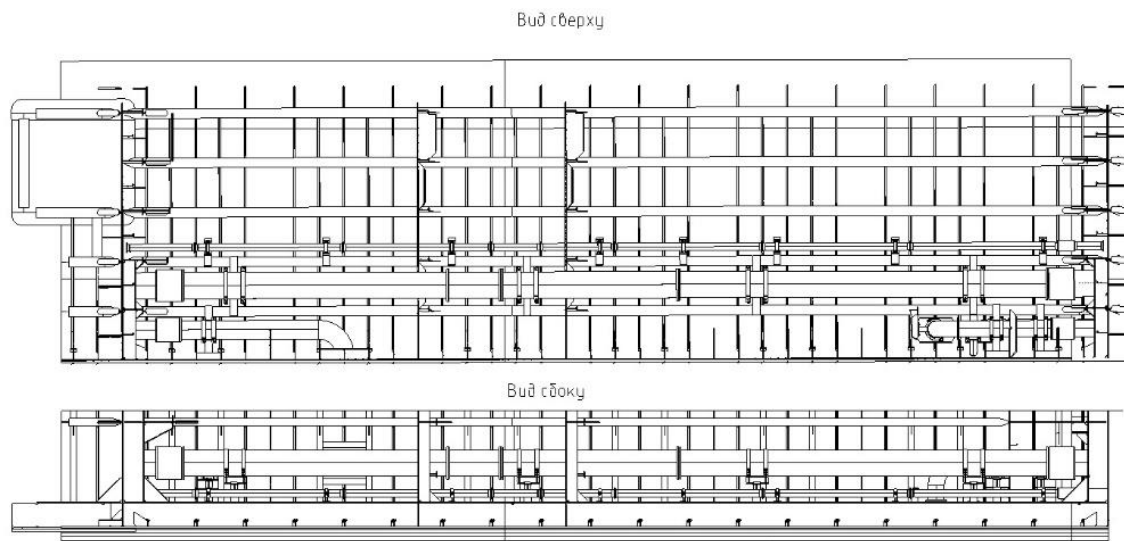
Заготовка под чертеж балластной и зачистной системы в БО
